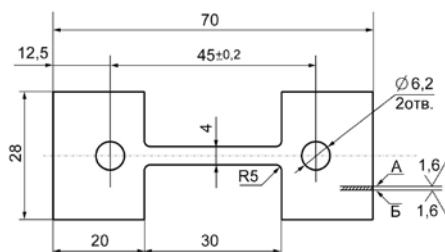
Зразок для визначення механічної поведінки поверхневих НКС
